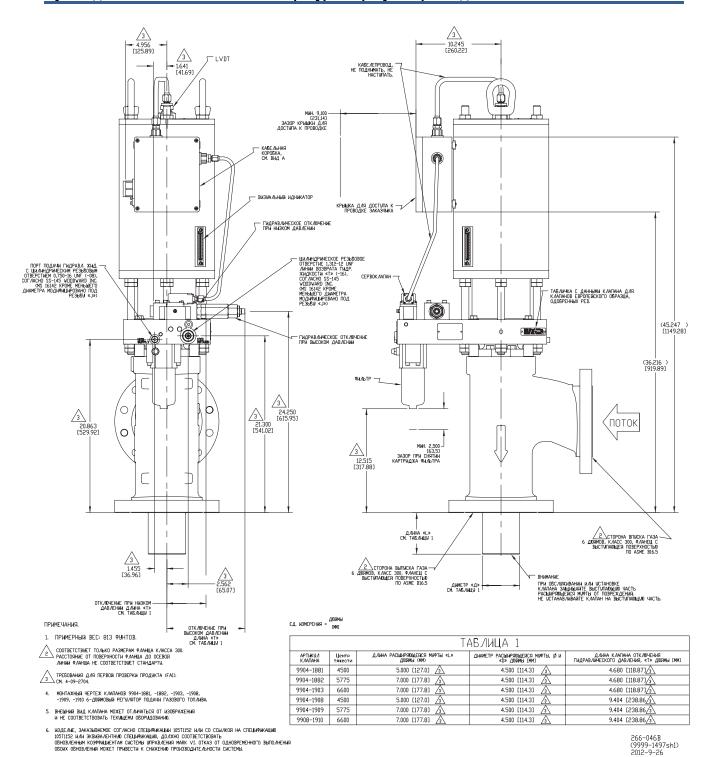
Габаритный чертеж регулятора SonicFlo (6 дюймов, класс 300)
